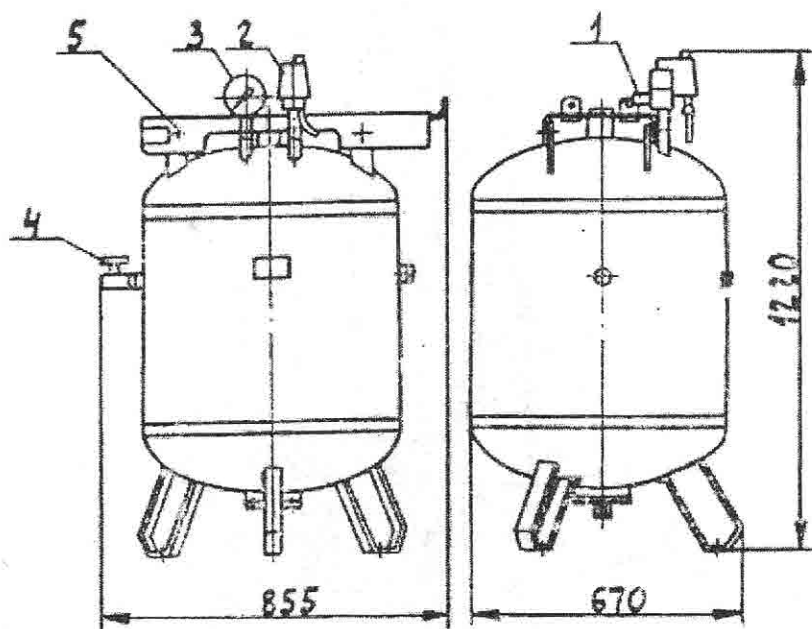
Ресивер установки компрессорной, модель KB-15:
